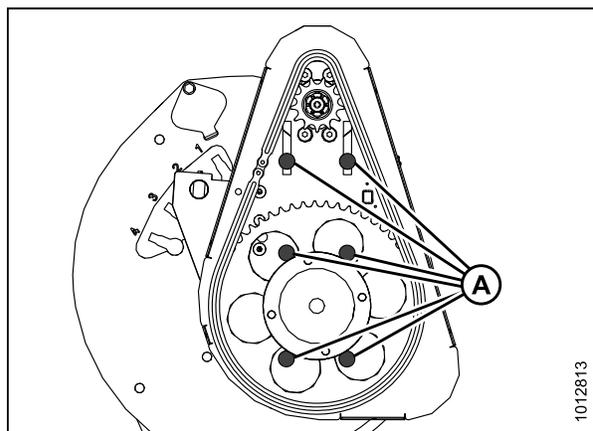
Изображен привод единого мотовила — привод сдвоенного мотовила имеет такую же конструкцию
